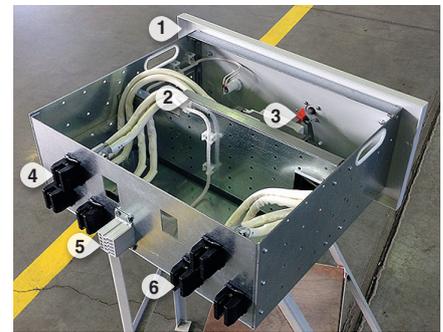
Компоновка выдвижного блока: 1 – основа выдвижного блока; 2 – держатель аппаратов; 3 – приводной механизм; 4 – выходные контакты; 5 – разъем цепей управления; 6 – контакты питания
